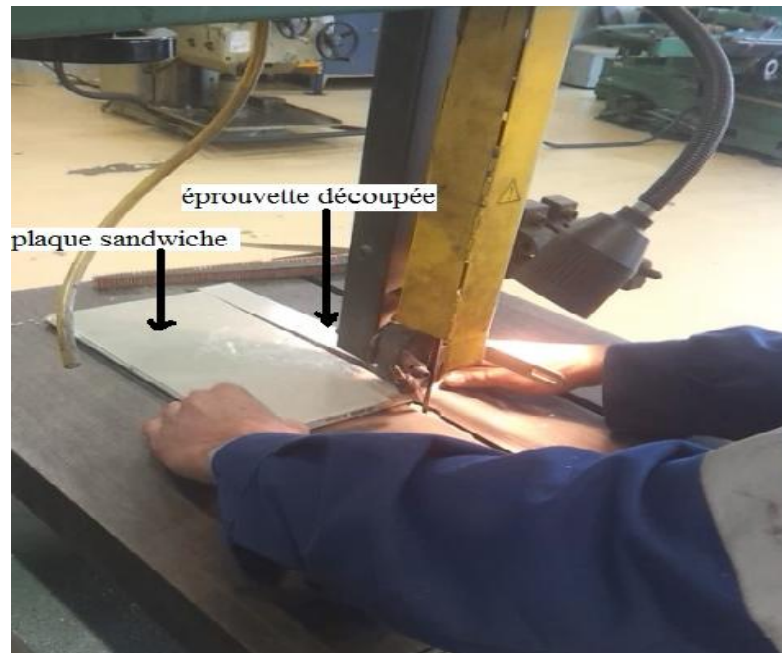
Opération de découpage de la plaque sandwichs en éprouvettes
